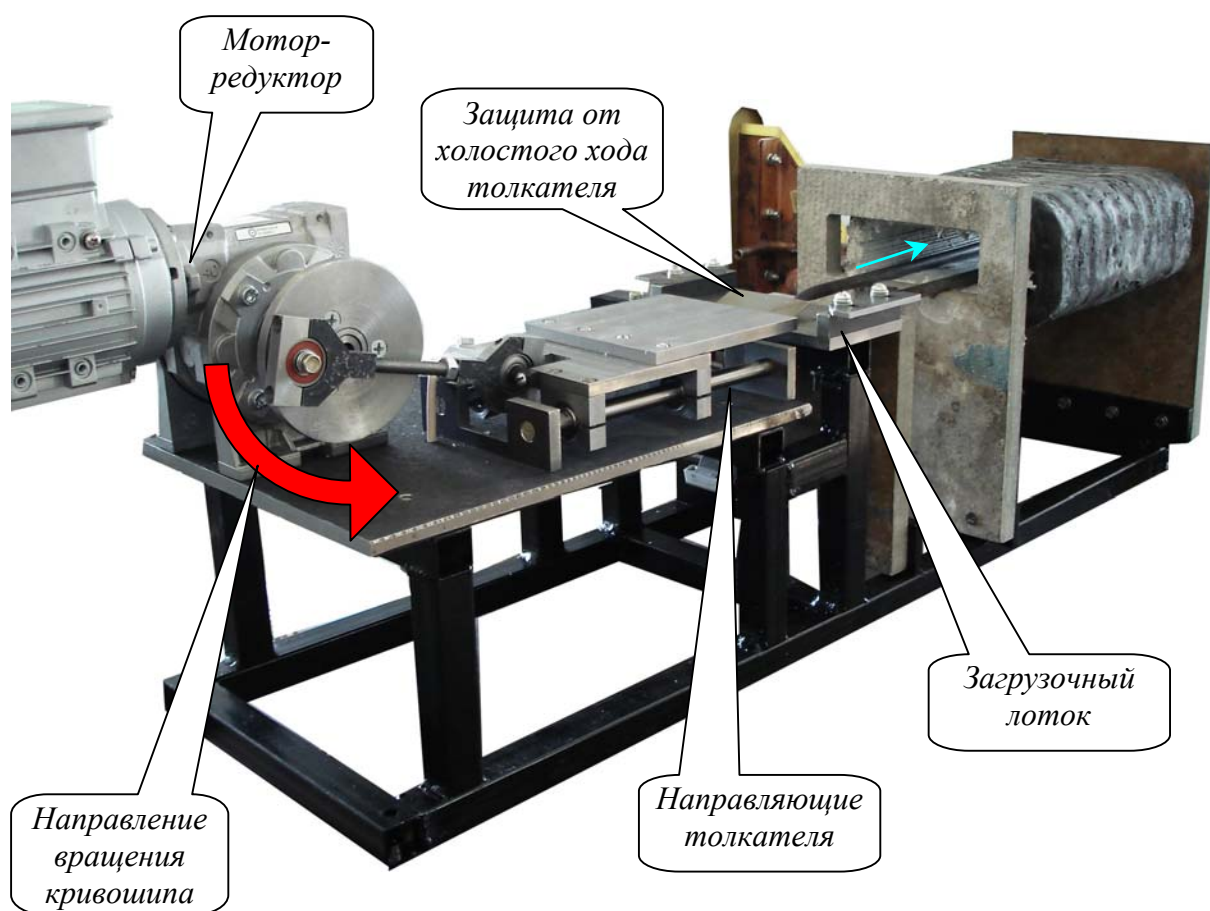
Устройство подачи заготовок в индуктор (общий вид)
